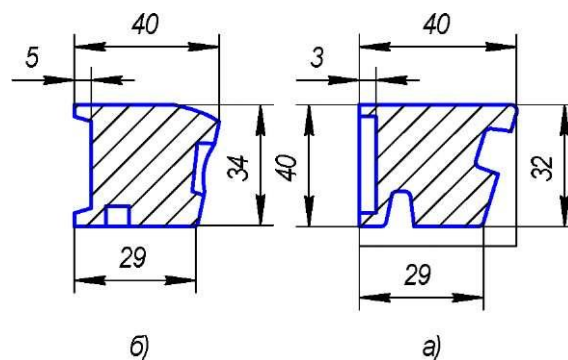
Заготовки висувного долота: а - з фрезерованим пазом під наплавлення; б - з прокатним пазом
